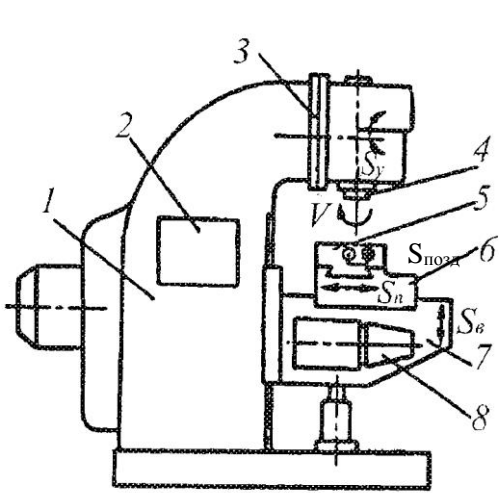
Загальний вид вертикально-фрезерного верстата
